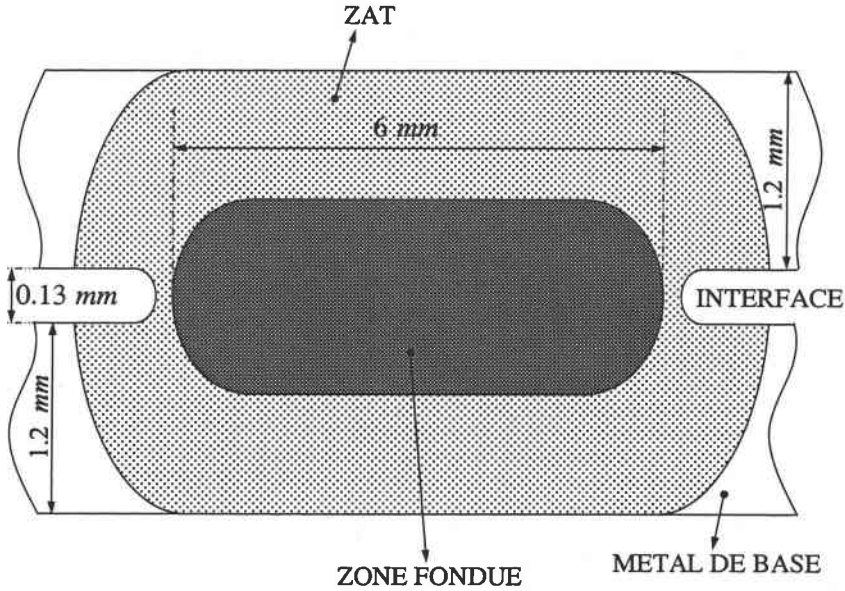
Schéma de la géométrie du point soudé pour la taille du point soudé, de l'interface et de l'épaisseur.
